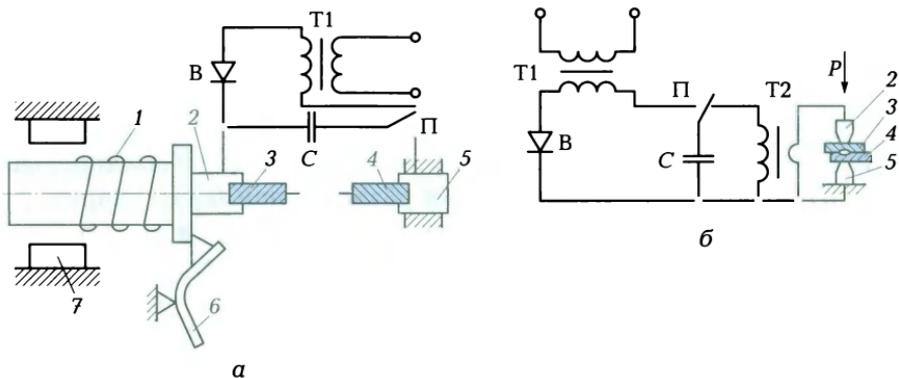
Схемы конденсаторной сварки:
